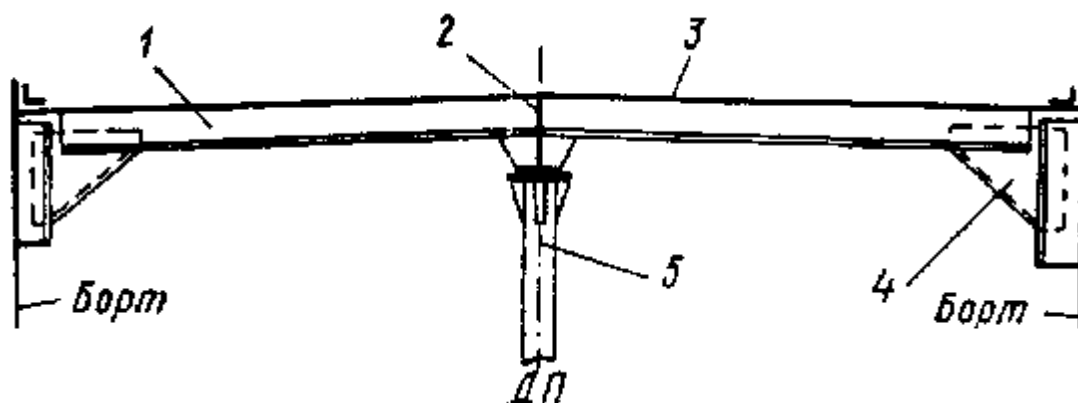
Конструктивные элементы палубного перекрытия:
